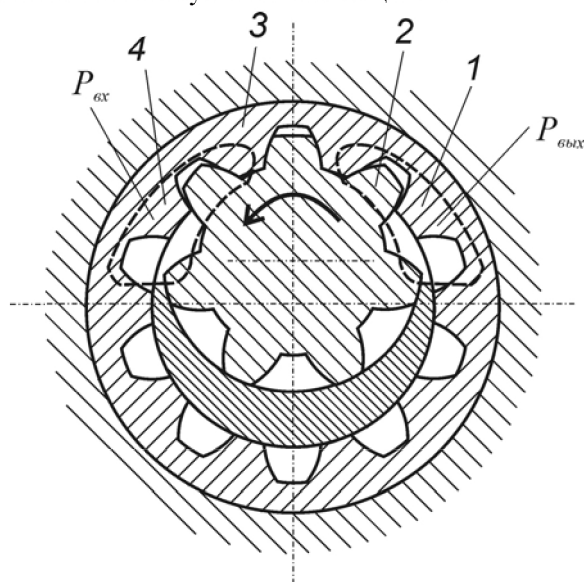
Шестеренный насос с внутренним зацеплением
